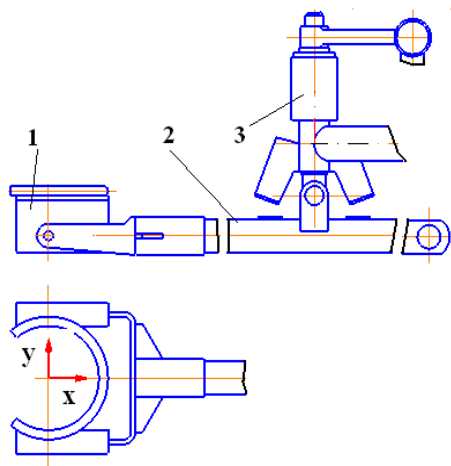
Захват манипулятора для защиты струи металла при разливке на МНЛЗ:
